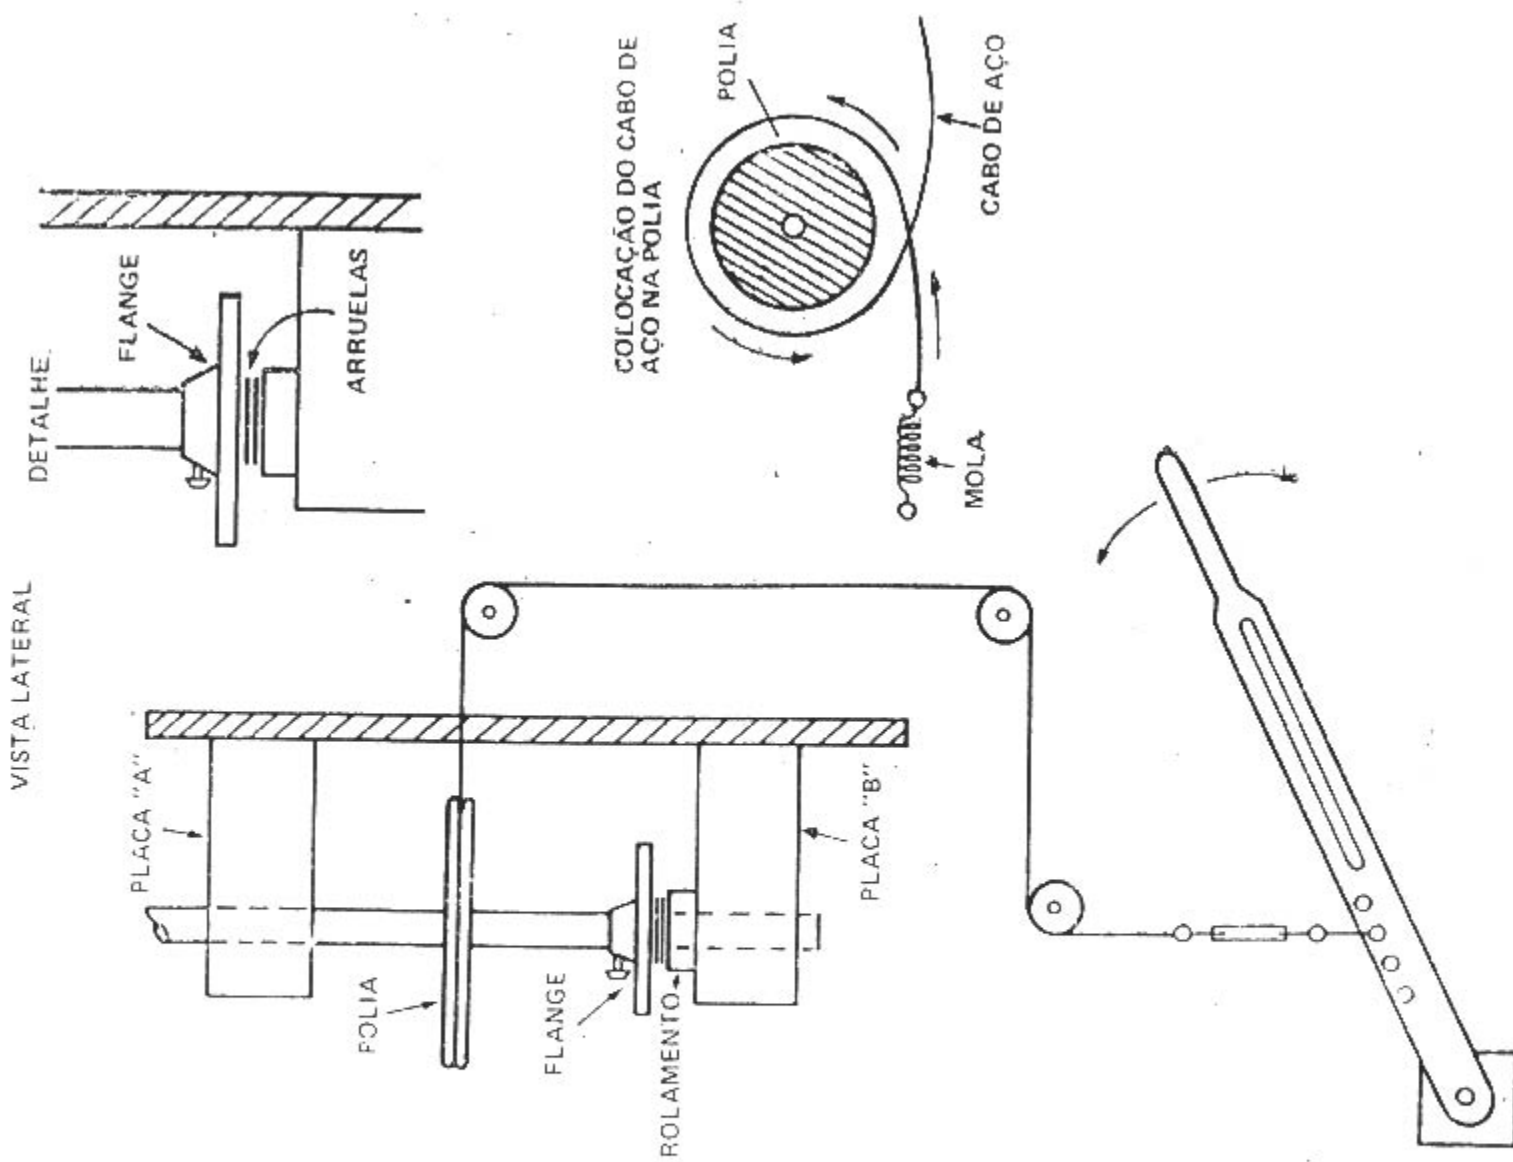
Plano geral do sistema de rotor manual de antenas. O tubo de ferro galvanizado, para a fixação da antena, é introduzido na placa A, polia, flange, rolamento e placa B. O flange fica apoiado na parte central do rolamento. Da polia sai um cabo de aço que vai ter ao marcador/alavanca. Em detalhe acha-se representada a forma de se calçar o flange com arruelas; para que o apoio seja feito sobre a parte central do rolamento; também vemos em detalhe como deve ser colocado o cabo de aço na polia.
